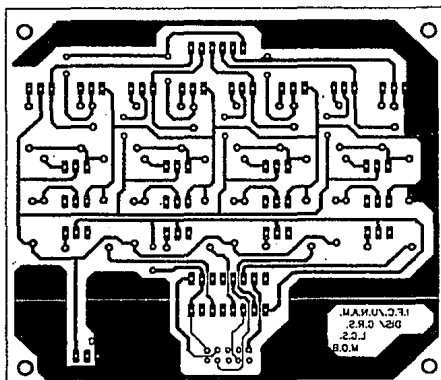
La cara de soldadura del circuito impreso.
